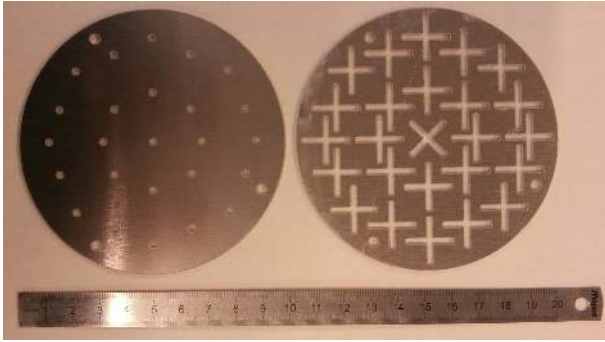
Photo des deux types de plaques utilisées pour assembler le matériau étudié
